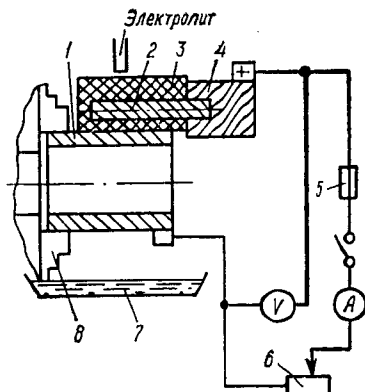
Схема установок для хромирования крупногабаритных деталей:
